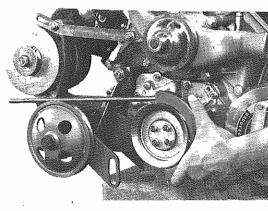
Allineamento puleggia alb. motore-pompa servosterzo Alignment of crankshaft power steering pump pulleys
